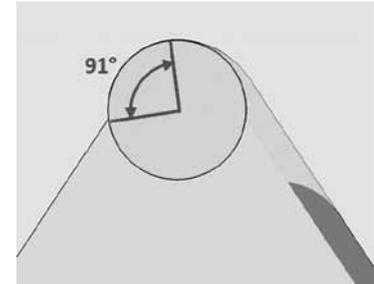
При обработке внутренних углов происходит увеличение угла перекрытия, что приводит к повышению нагрузки на станок и инструмент
